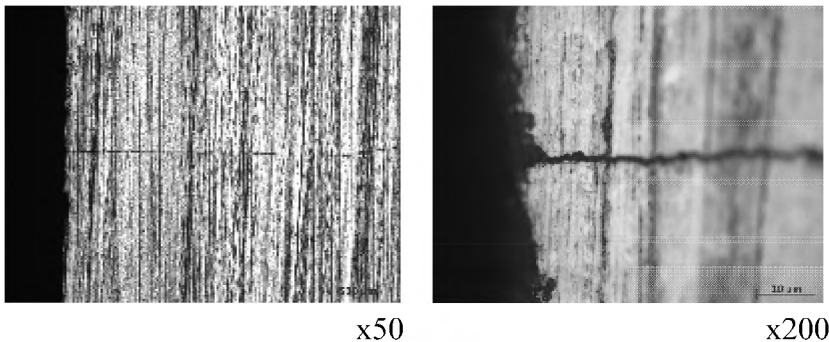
Загальний вид передніх поверхонь твердого сплаву марки ВК8 після заточування колами з карбиду кремнію
